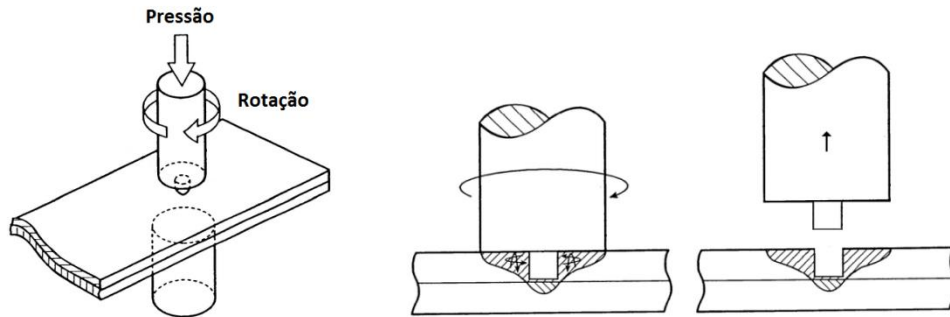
Ferramenta para soldagem Plunge FSSW indicando direção de rotação, pressão, movimentação vertical e área soldada resultante (IWASHITA 2003).
